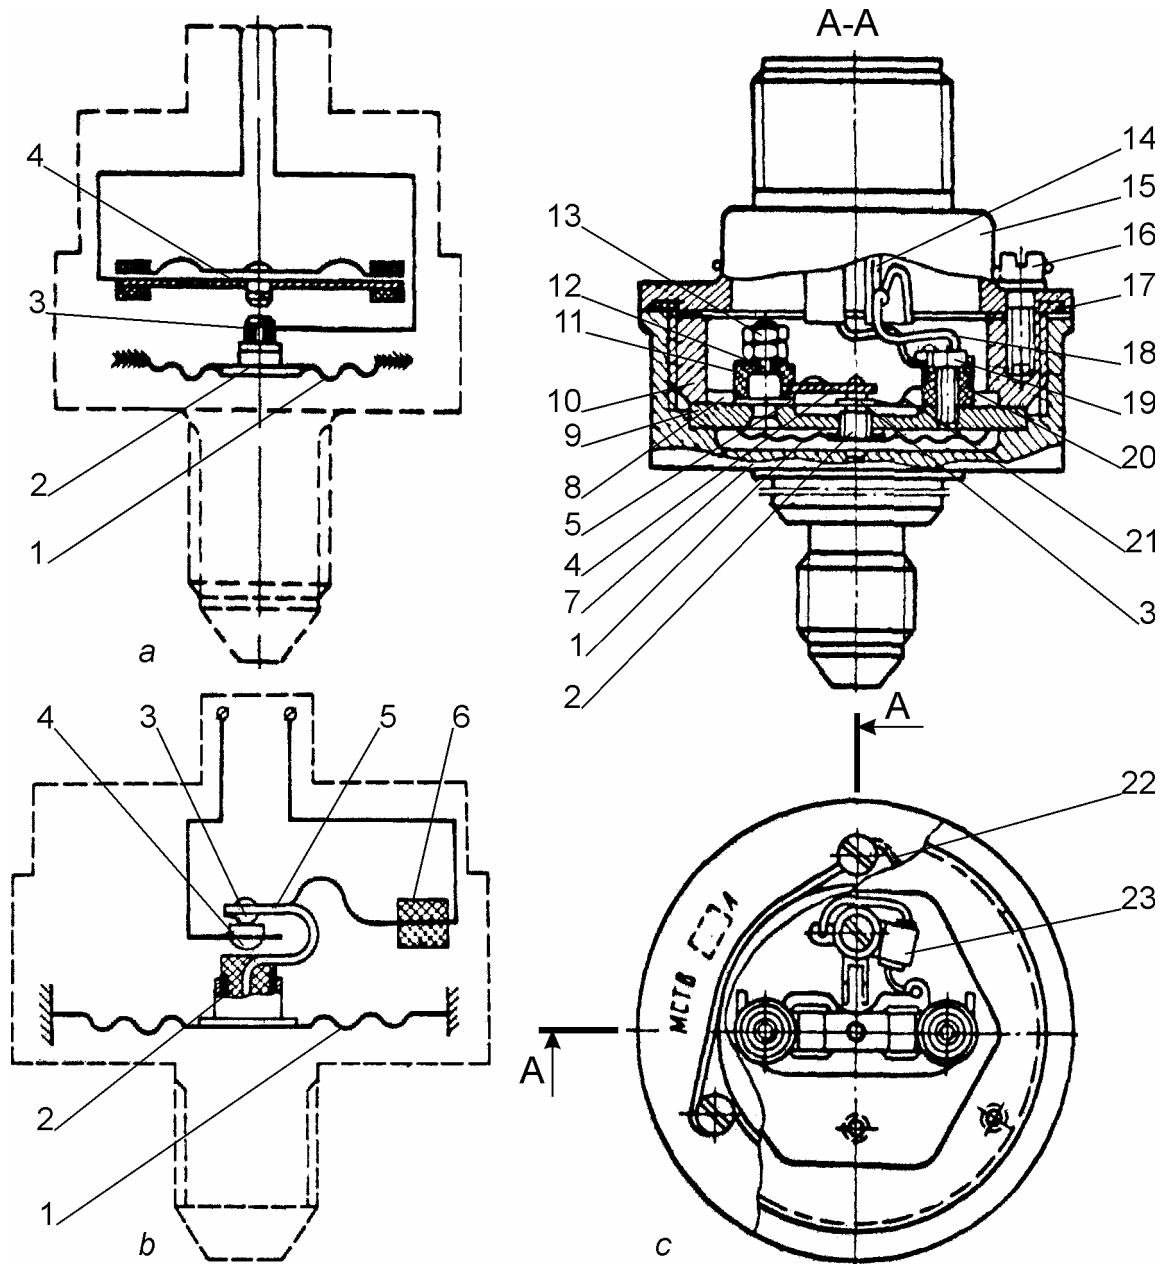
Сигналізатори тиску: а — схема сигналізатора МСТВ-А; б — схема сигналізатора МСТВ; в — конструкція сигналізатора МСТВ-А; 1 — мембрана; 2, 6, 11, 20 — ізолятори; 3 — рухомий контакт; 4 — нерухомий контакт; 5 — пластина; 7 — корпус; 8 — шайба; 9 — упор; 10 — кришка; 12 — шпилька; 13 — гайка; 14 — вилка; 15 — кожух; 16, 19 — гвинти; 17 — прокладка; 18, 21 — провід; 22 — контрвальний дріт; 23 — косинець
